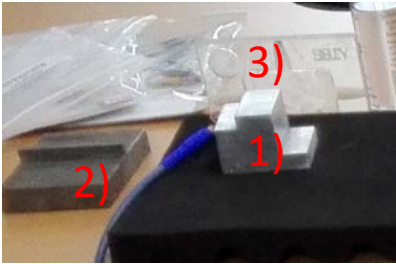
Ejemplos de probetas de calibración fabricadas: 1) Aluminio; 2) Acero; 3) Acrílico.
